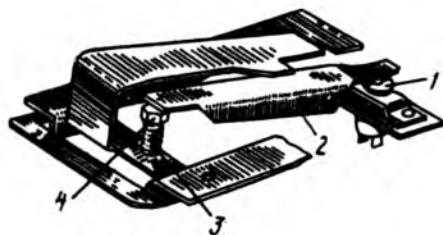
Автоматический выключатель сажалки САЯ-4: 1 - кнопка выключателя; 2 - клапан датчика; 3 - пружина; 4 - гайка
